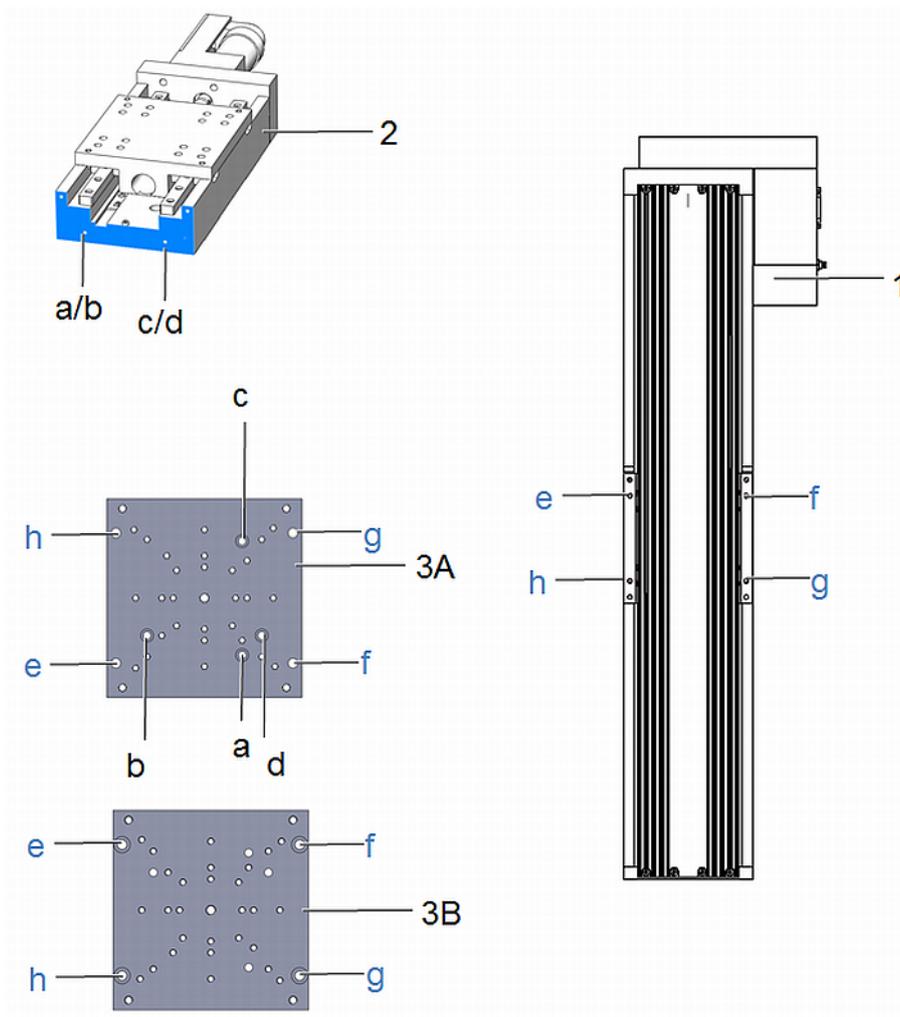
Bohrungen zur Befestigung der Z-Achse
